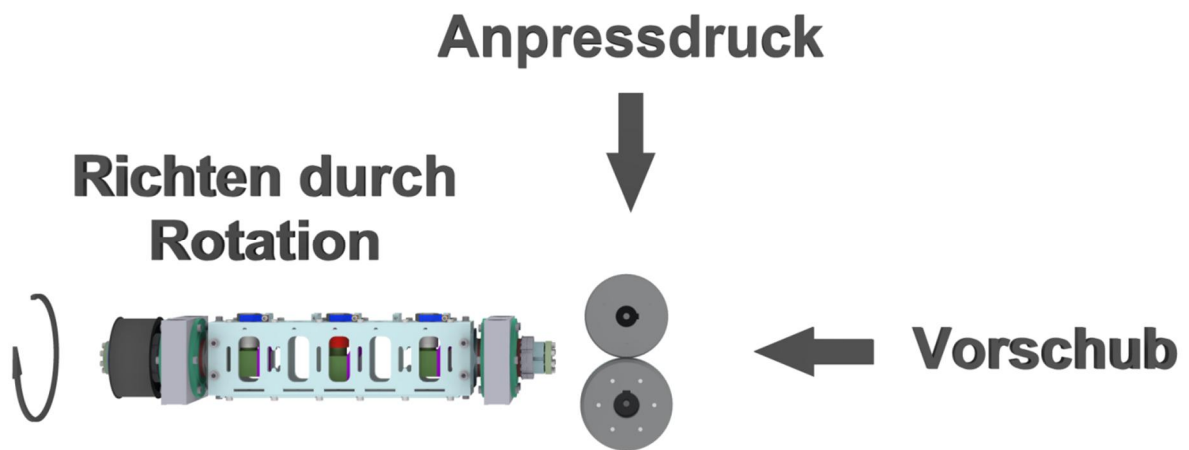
Prinzip des Richtens von Bewehrungsstahl mit Rotortechnik
